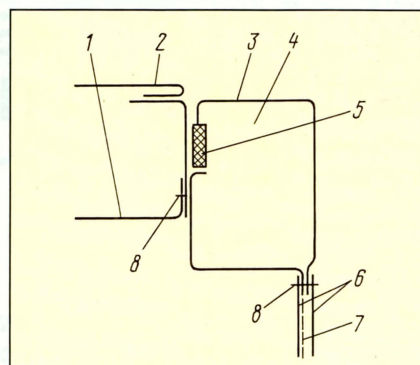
Фрагмент двери рабочей камеры: 1 — стенка рабочей камеры; 2 — кожух; 3 — металлический корпус двери; 4 — дроссельная полость; 5 — дополнительный поглотитель энергии СВЧ; 6 — полимерная пленка; 7 — перфорация; 8 — сварка
